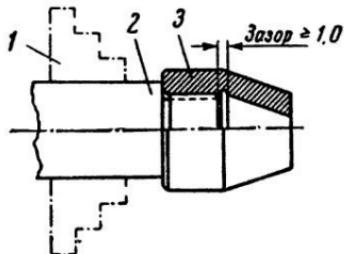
Патронная оправка для обработки деталей с внутренней резьбой (типа гаек):
